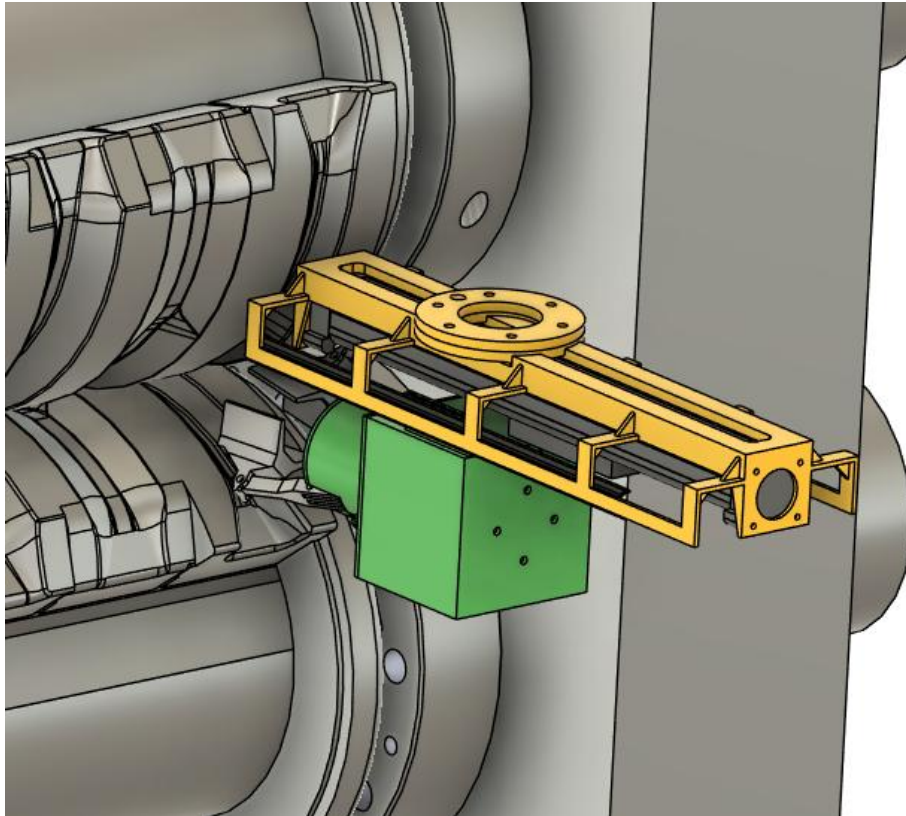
Vista de la posición del conjunto efector final y amortiguador durante la aproximación a los moldes en la roladora.
